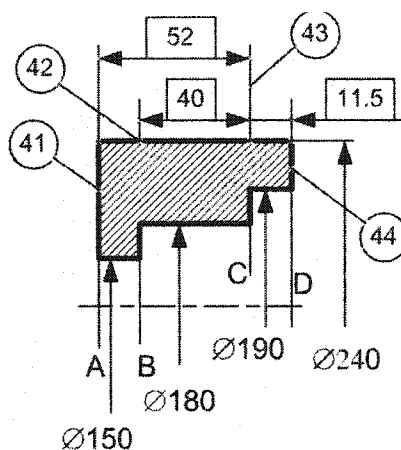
Extrait (pour la pièce 4) des dimensions fonctionnelles des pièces (composants) [ZHANG-96]
